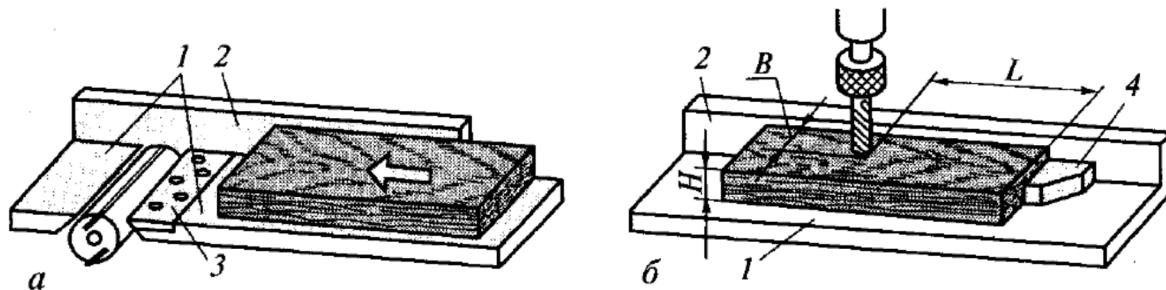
Рухоме (а) та нерухоме (б) базування заготовок при деревообробці:
